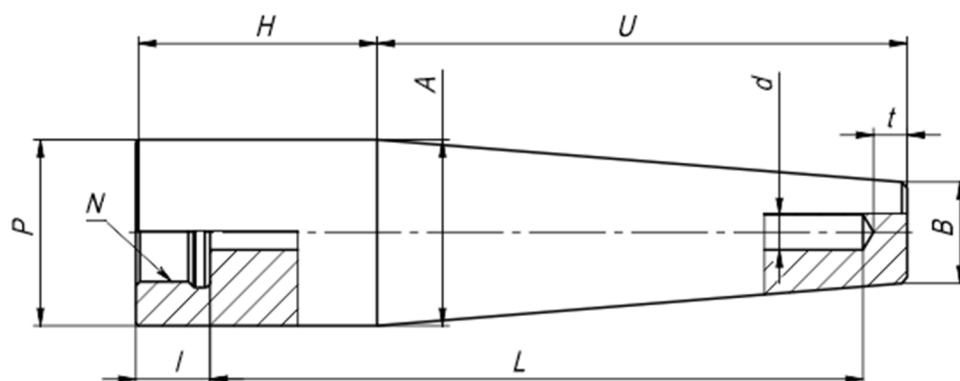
Гильза под приварку в стенку трубопровода (Weld-in), цельноточёная, коническая, под подвижный штуцер.
